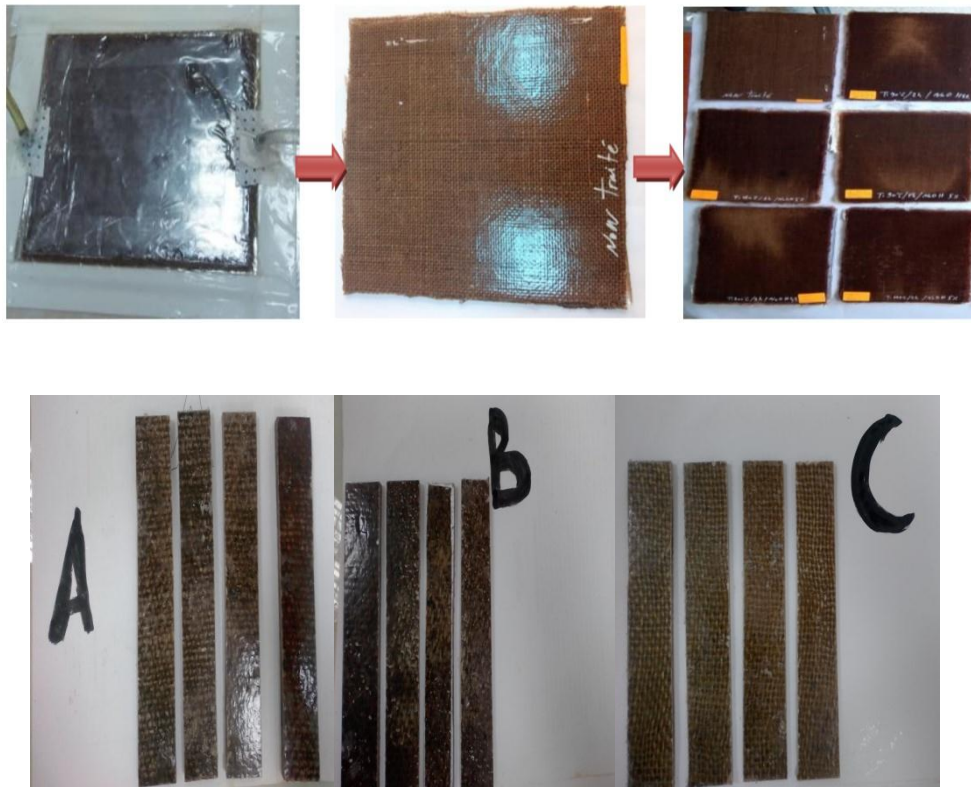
Les dimensions des éprouvettes. (ASTM3039)
